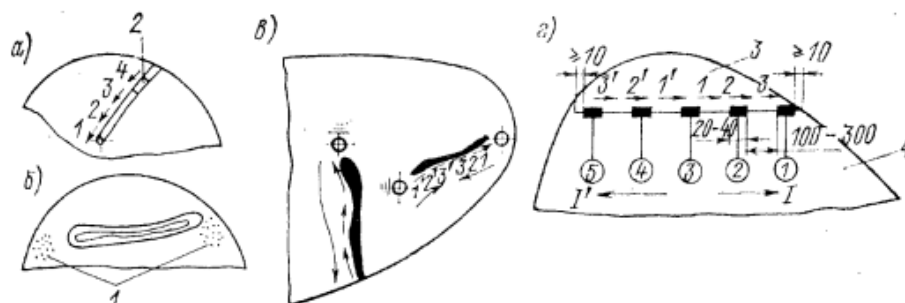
Ремонт лопаті: а - обробка з установкою клину; б - правка; в - заварювання; г - установка наделки 1 - місця підігріву; 2 - клин; 3 - наделка; 4 – лопатя
